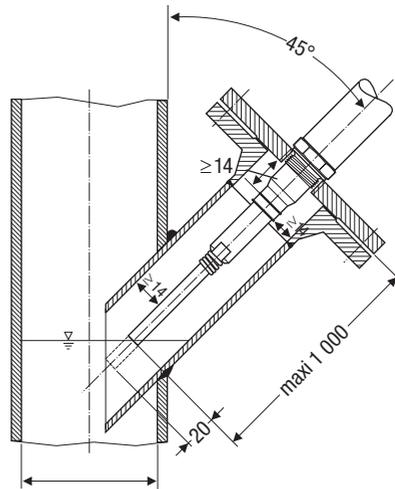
Montage en position inclinée, par ex. dans les conduites de départ montantes d'installations à eau surchauffée ou dans des réservoirs
